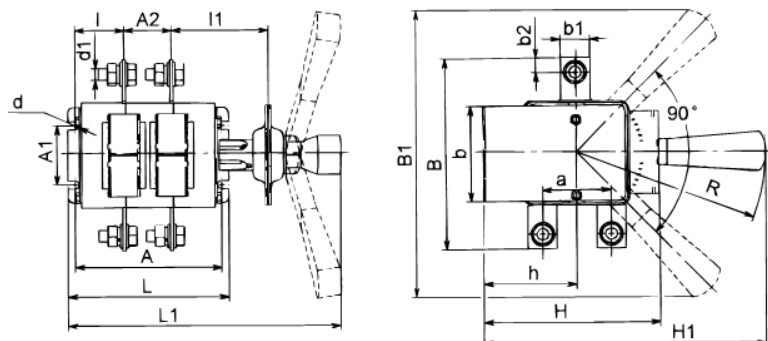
Б Выключатель-разъединитель на два направления двухполюсный с боковой смещенной рукояткой
